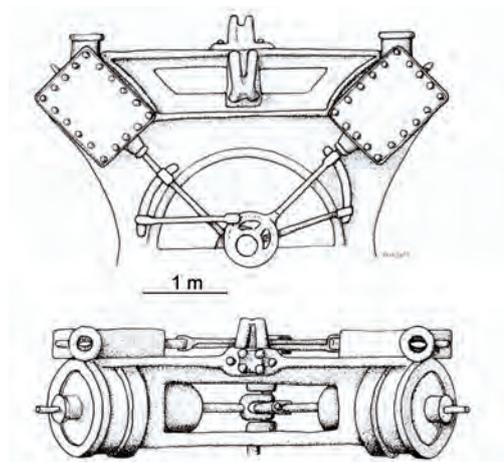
Le moteur du vapeur (Dessin M. Huet)
